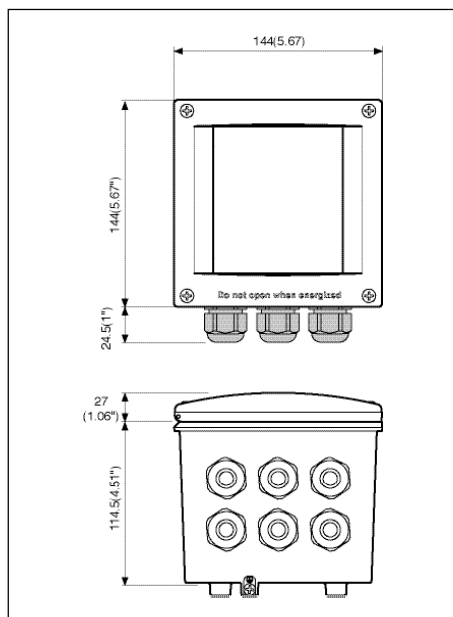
Dimensions de l'ensemble et emplacement des presse-étoupe
